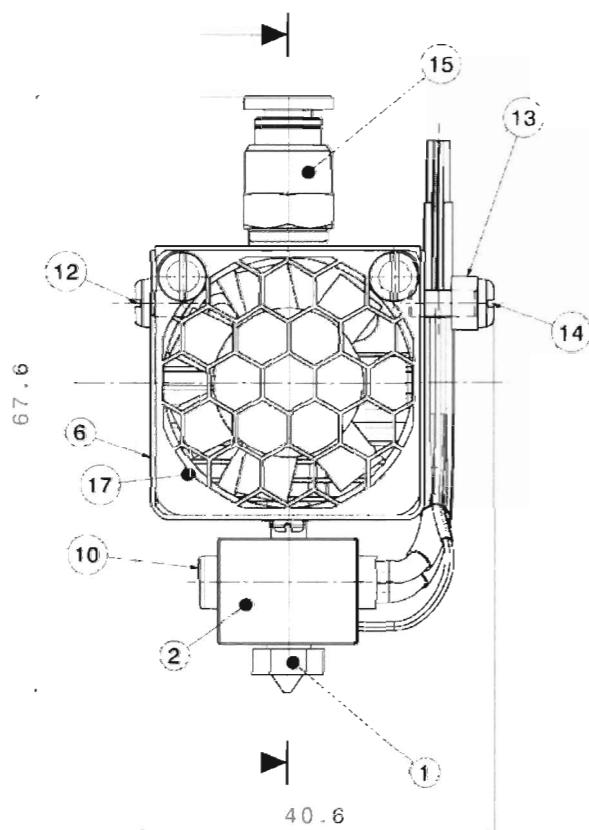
Ansamblul cap imprimare, echipat cu radiator bimetalic în sistem Bowden, vedere frontală
